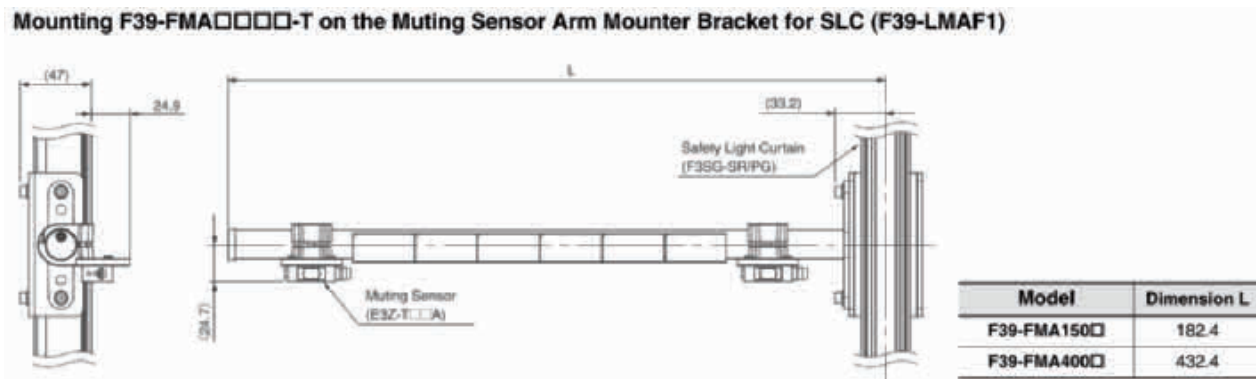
Fissaggio braccetti di muting sulla barriera con staffa F39-LMAF1
